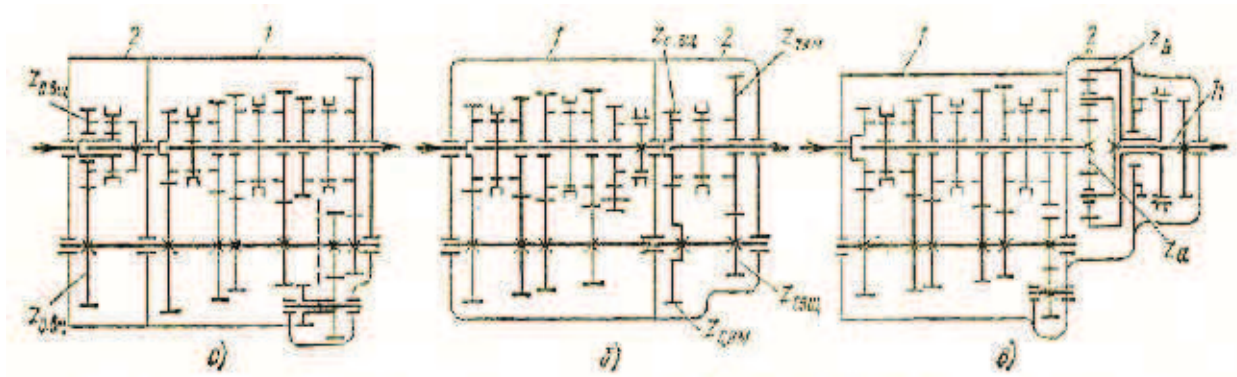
Схемы многоступенчатых коробок передач с дополнительными редукторами и тремя степенями свободы:
